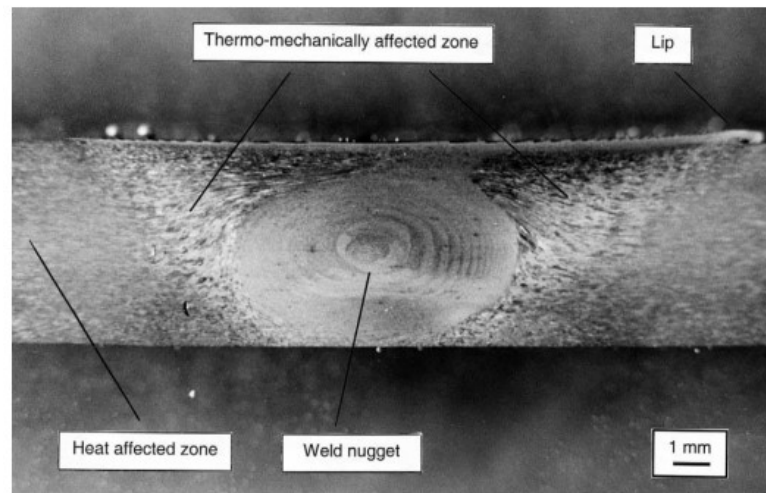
Macrostructure d'un joint soudé par friction malaxage [7]
